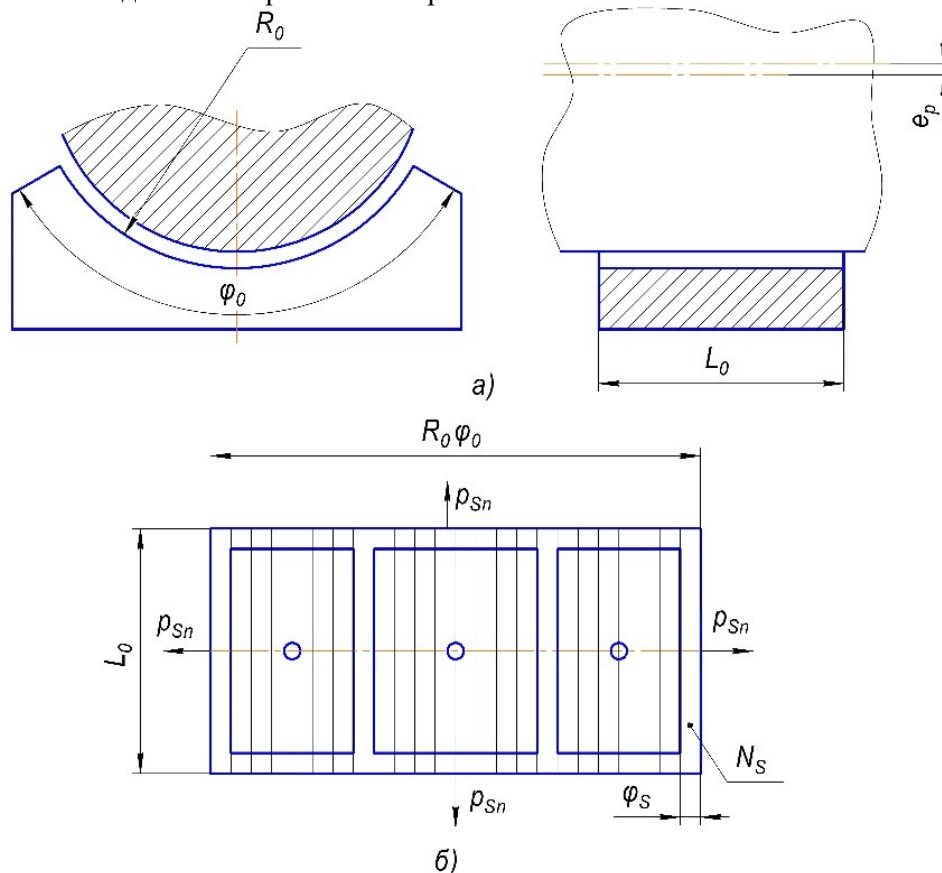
Гидростатический подшипник с неполным углом обхвата:
